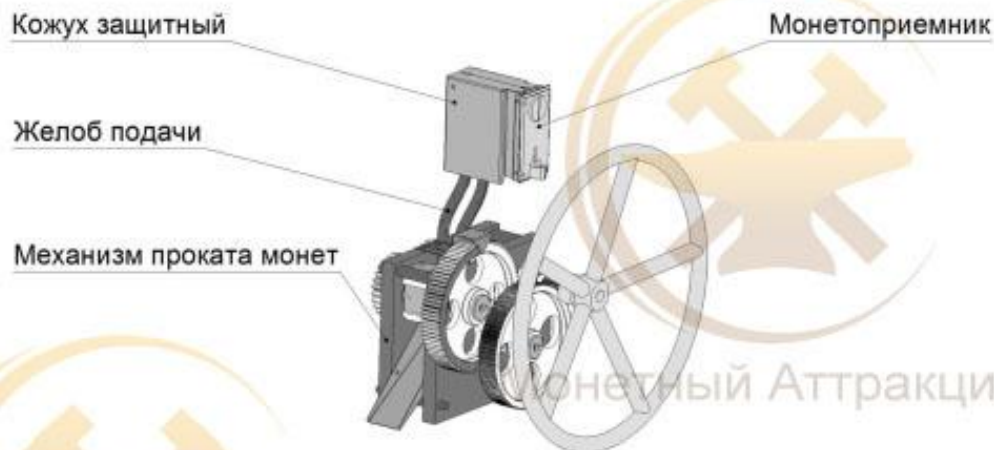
Общий вид органов подачи заготовки совместно с механизмом проката
